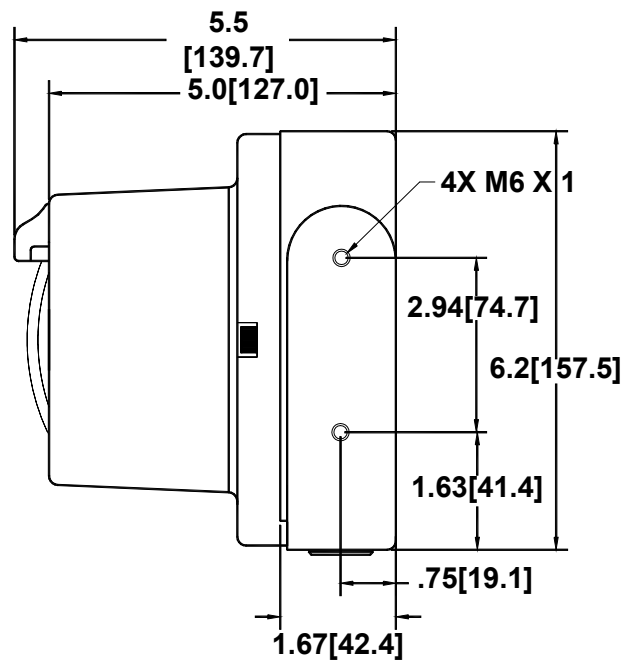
Габаритный чертеж FlameGard 5 UV/IR
